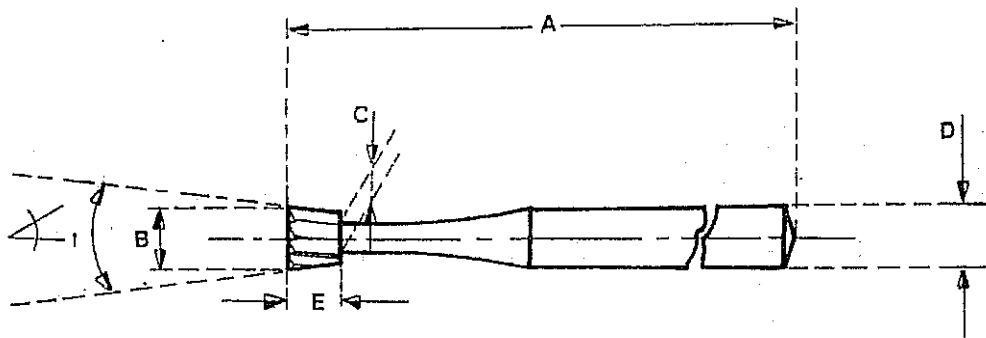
Fresas de carburo, forma cono invertido (claves: 060.431.0433, 060.431.0490, 060.431.0508, ~
